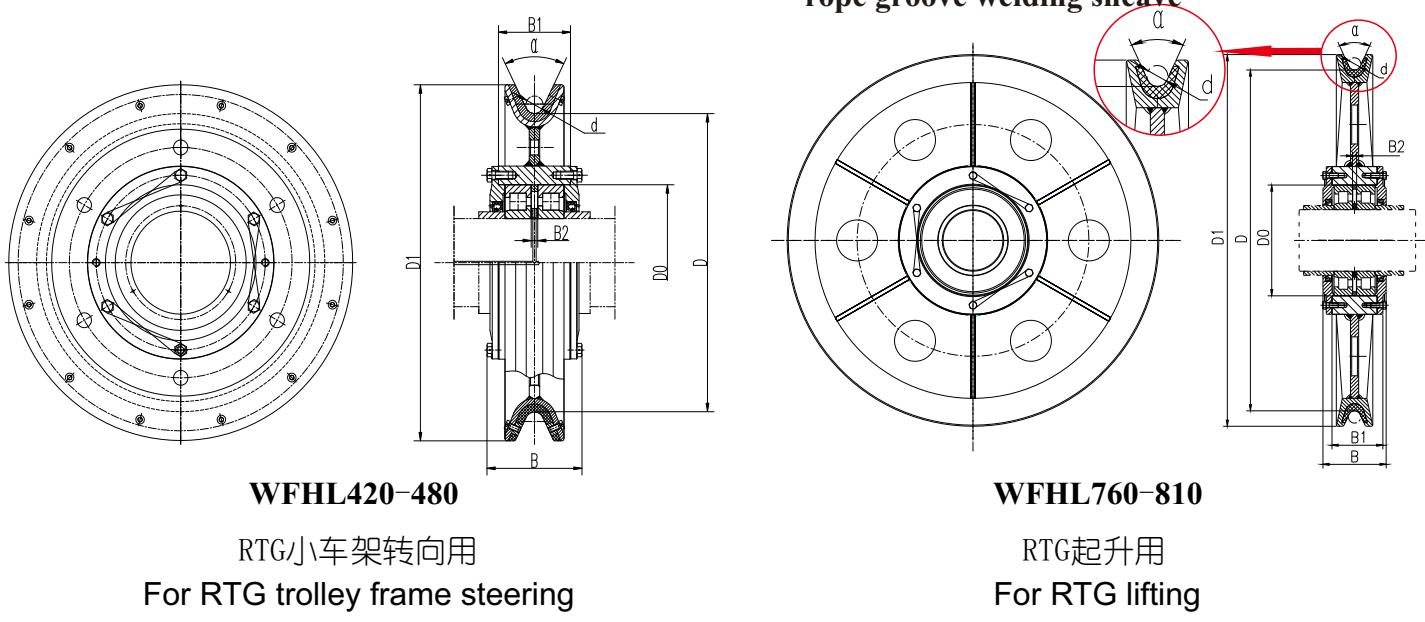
复合绳槽焊接滑轮 Fig. 7 Composite rope groove welded sheave
